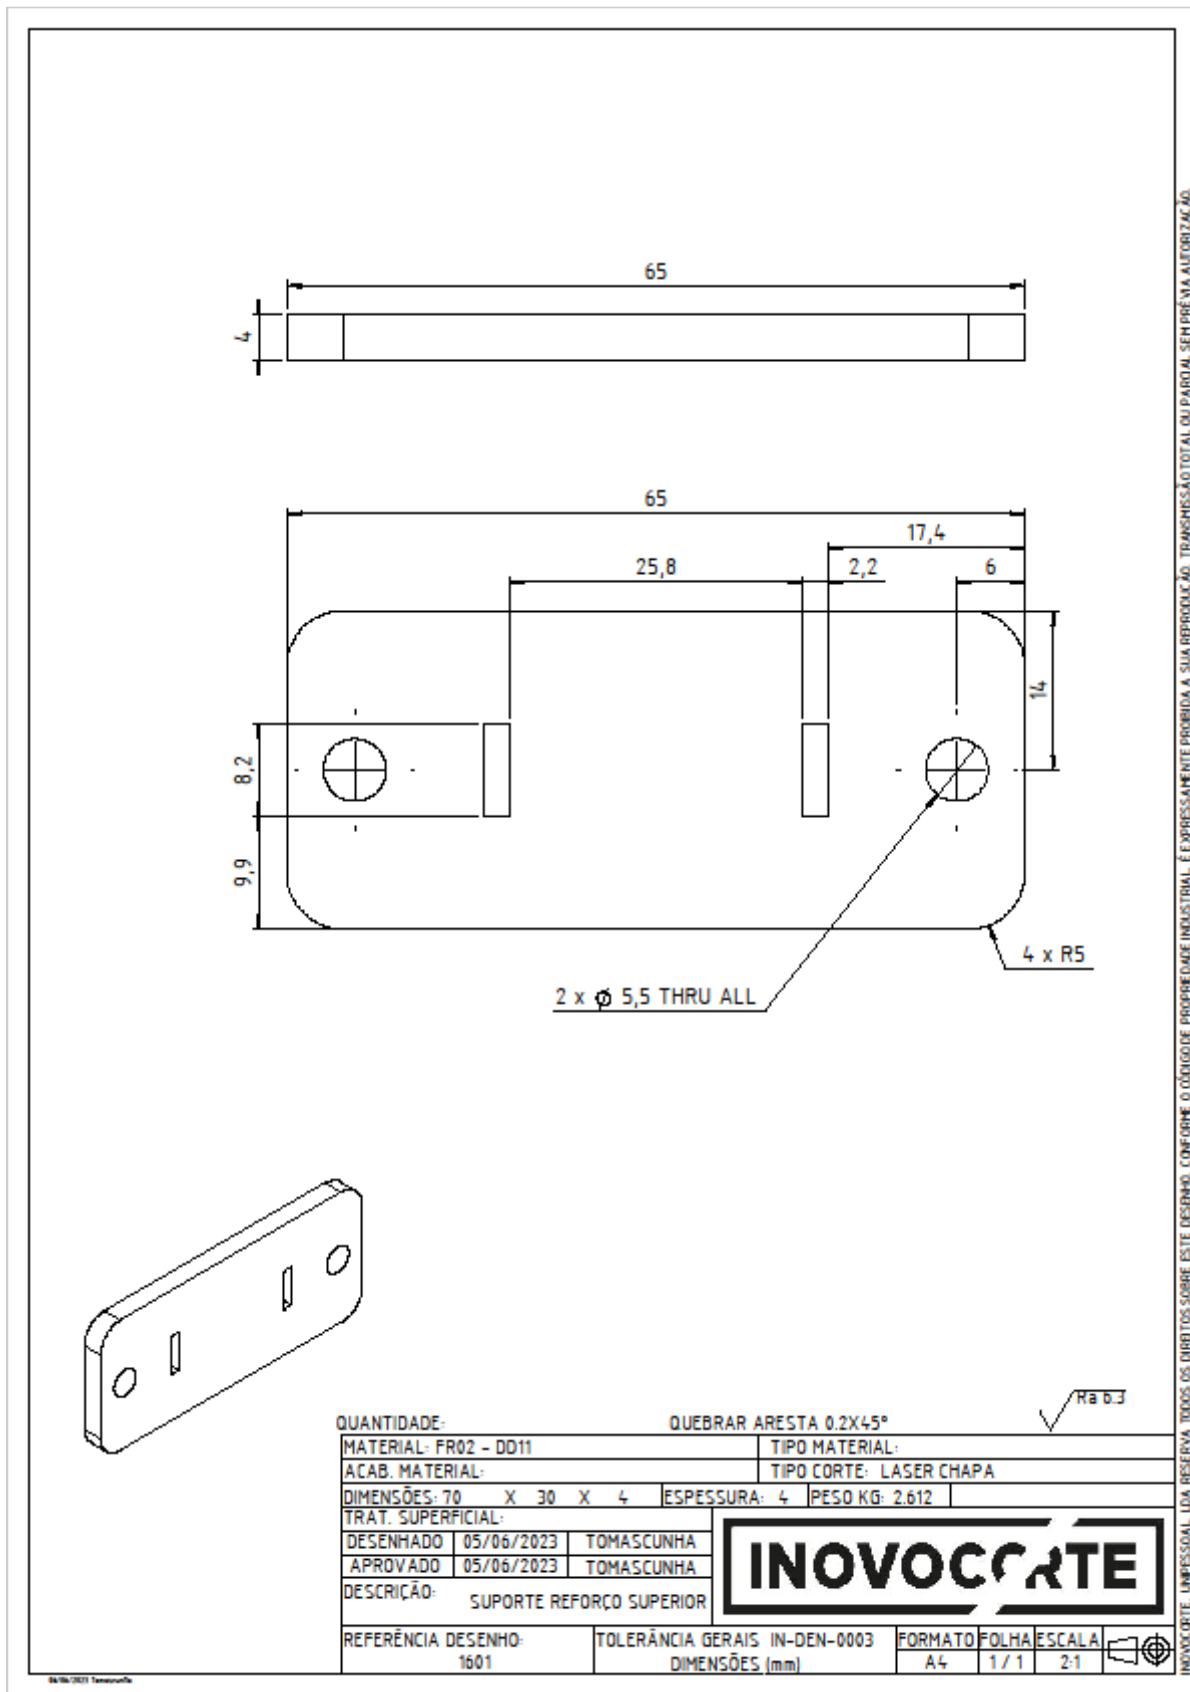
Desenho técnico do suporte reforço superior (1601).
